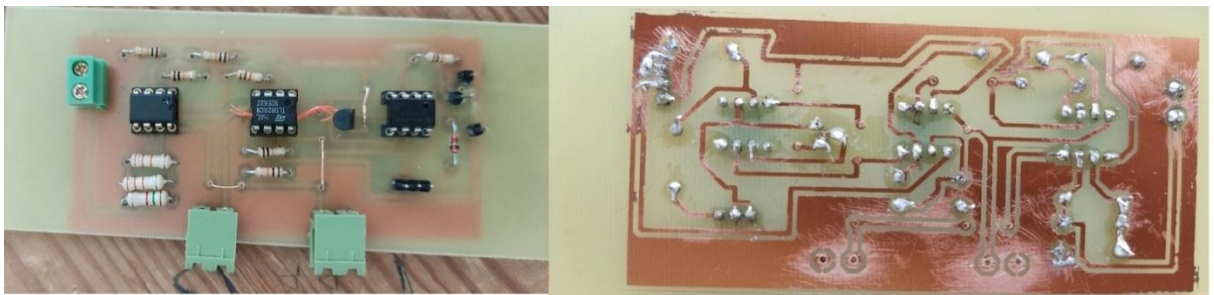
Circuit imprimé après soudure des composants
